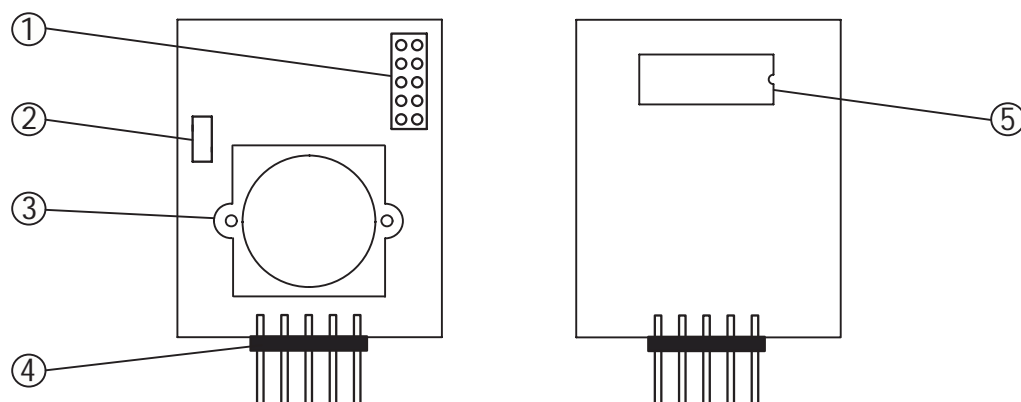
Détails du module HemLinCam : vue de devant et vue de derrière
